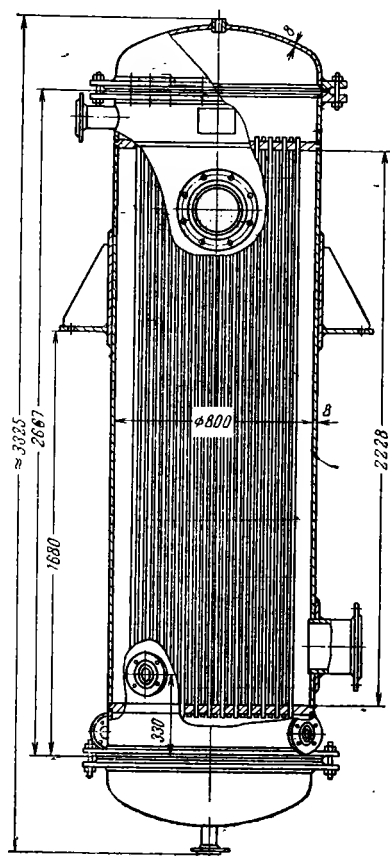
Вертикальный одноходовой дефлегматор с неподвижными трубными решетками.
